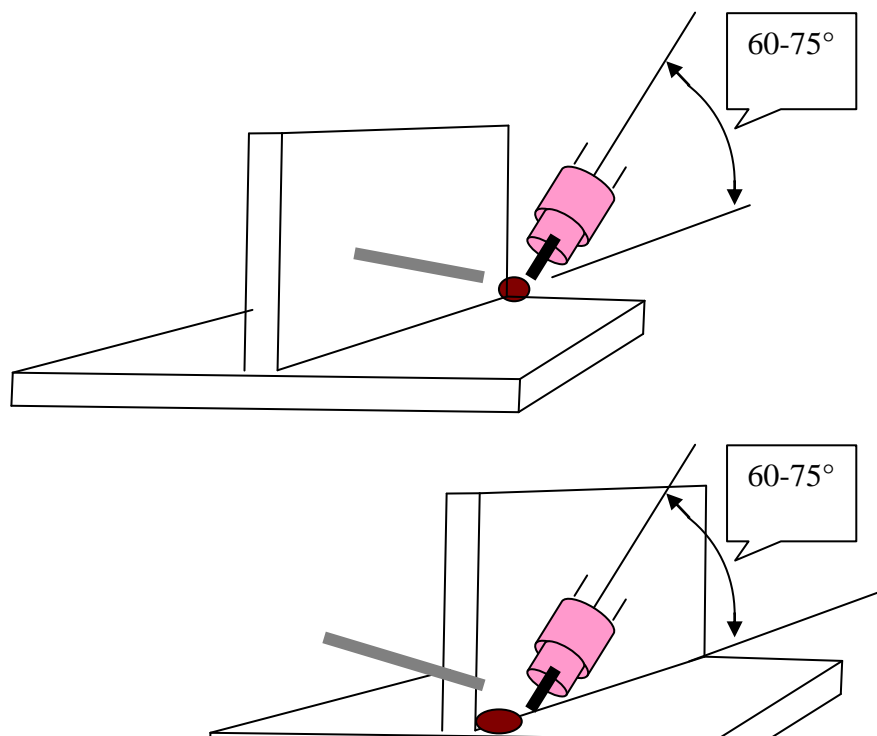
Punteado para obtener el ensamble de soldadura de filete.
